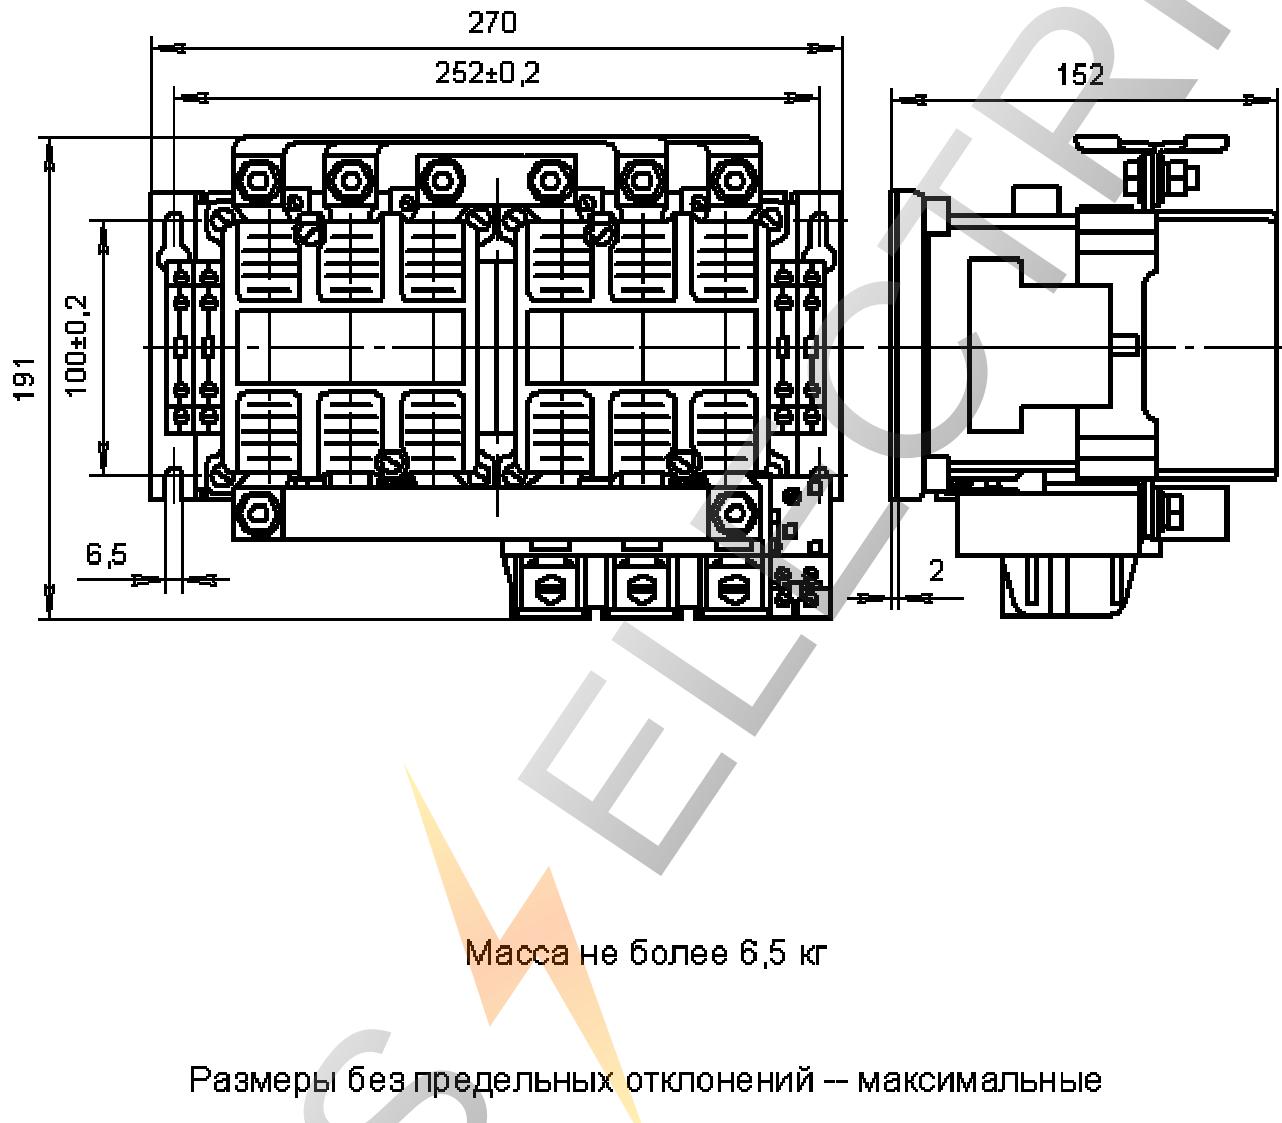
Пускатели реверсивные ПМ12-100600, ПМ12-125600
